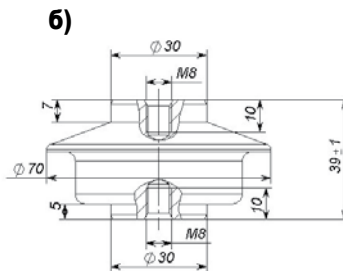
Габаритно-присоединительные размеры ОПНп класса напряжения 0,4
